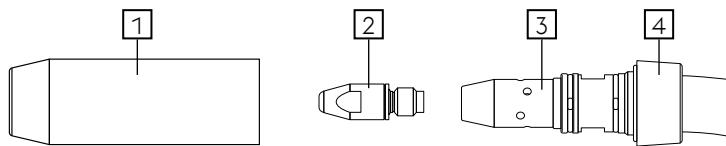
MT G ausrüsten / Setting up MT G / Équipement des torches MT G / Equipamiento de la MT G
